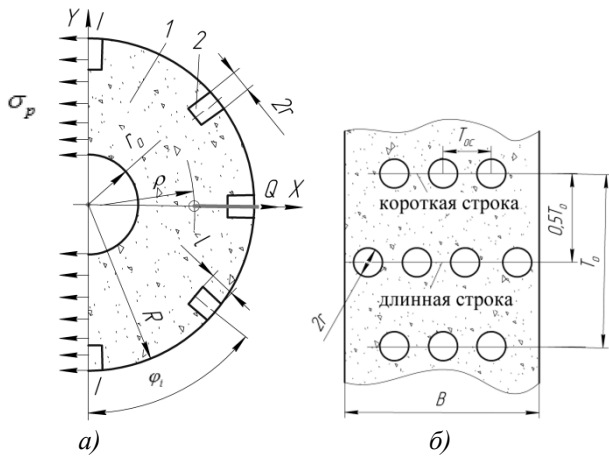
Дискретный шлифовальный круг под действием центробежной силы  $Q$  с отверстиями, расположенными:
